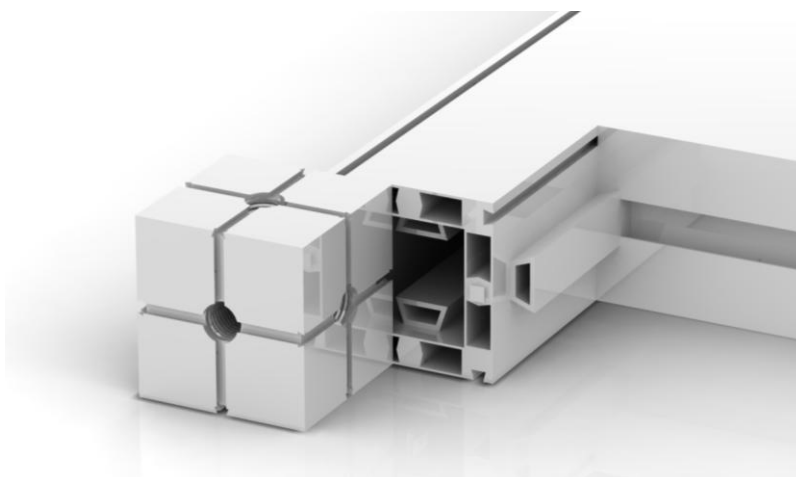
Sistema expositivo flexível – detalhe de encaixes. Fonte: Autor.
